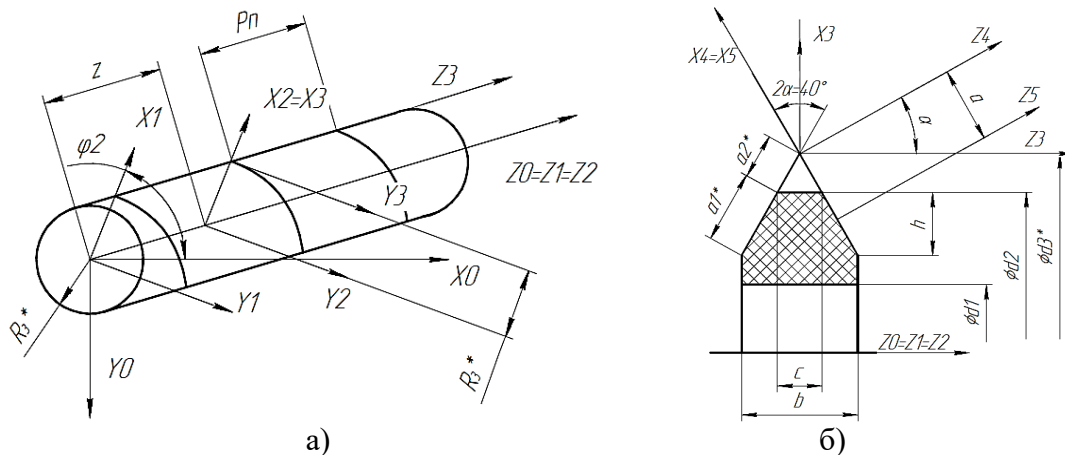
Схема взаємодії оброблюваної деталі і інструмента: а) вид зверху та б) вид збоку
